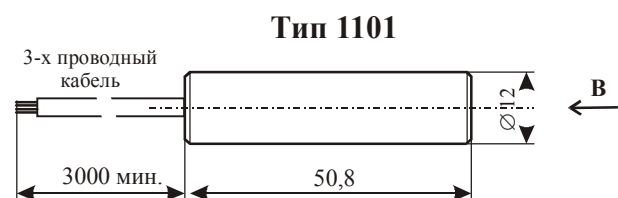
Внешний вид и габаритные размеры датчиков типа 1101
